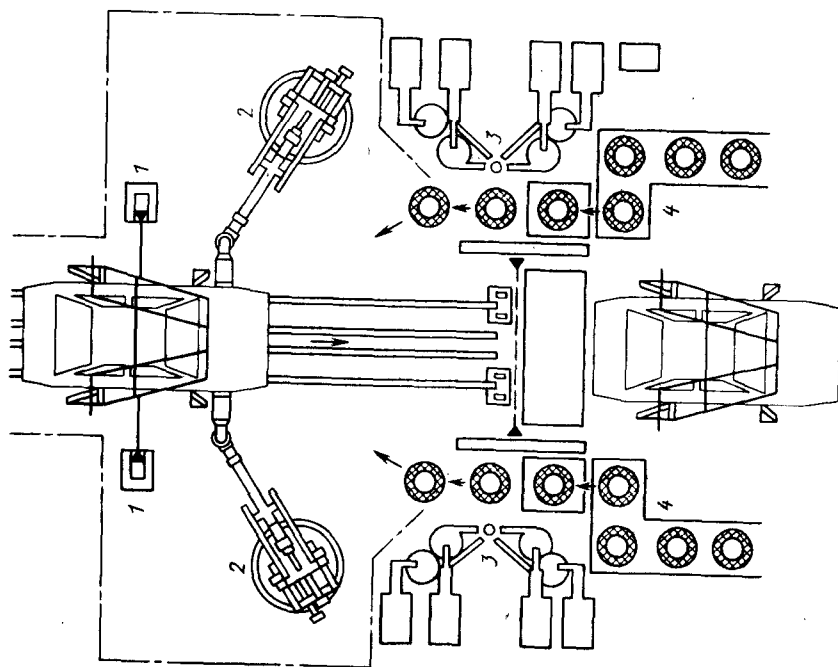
Роботизированный сборочный комплекс для установки автомобильных колес с использованием СТЗ:
